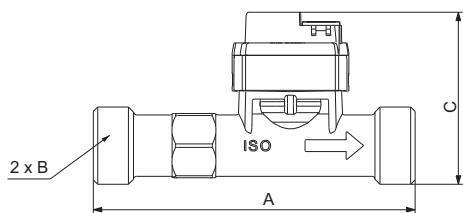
Размеры, VFS QT, 1-15 л/мин, резьбовые соединения
